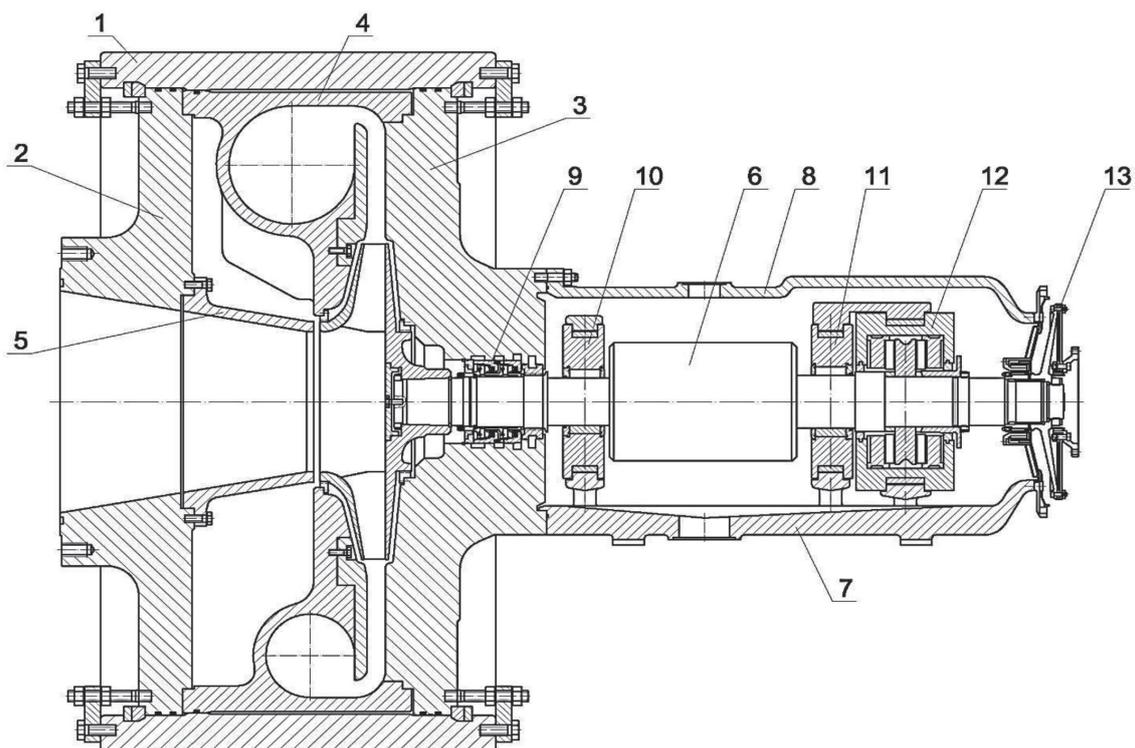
Продольный разрез корпуса сжатия одноступенчатого компрессора конструкции ПАО: 1 – корпус; 2 – крышка передняя; 3 – крышка задняя; 4 – улитка; 5 – проставка; 6 – ротор; 7 – корпус подшипников; 8 – крышка; 9 – ТГДУ; 10 – подшипник опорный передний; 11 – подшипник опорный задний; 12 – подшипник упорный; 13 – полумуфта.
